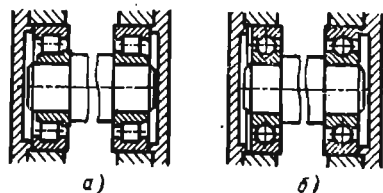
Схемы установки подшипников в опорах «плавающего» вала:
